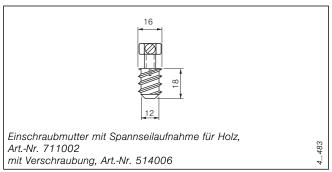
Einschraubmutter mit Spannseilaufnahme für Holz
